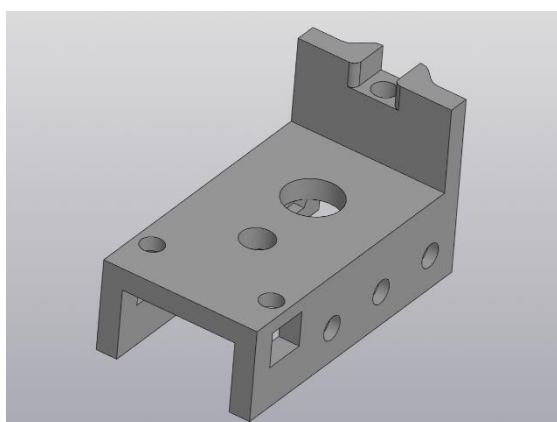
Модель крепления моторов (вид сверху)
